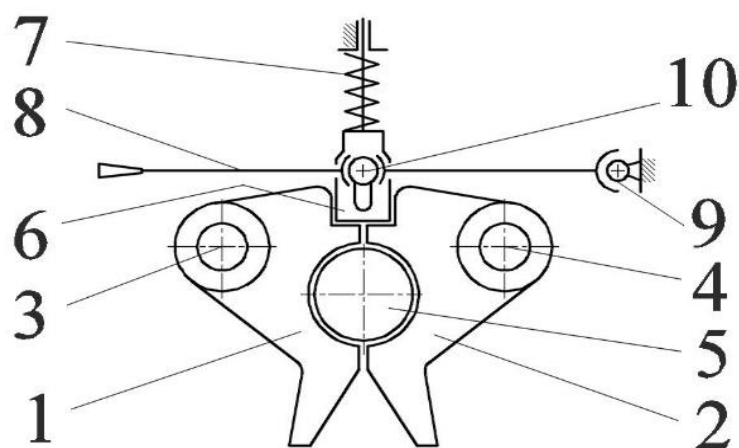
Схема запорного механізму сидельно-зчіпного пристрою.
